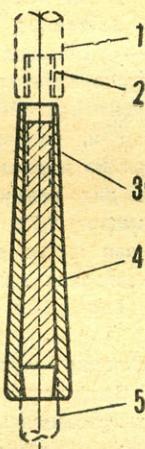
Механизм крепления ракеты к пусковой установке: 1 — гнездо для стержня, 2 — положение стержня во время пуска, 3 — бронзовая втулка, 4 — стальной стержень, 5 — соединение со стартовым двигателем.
